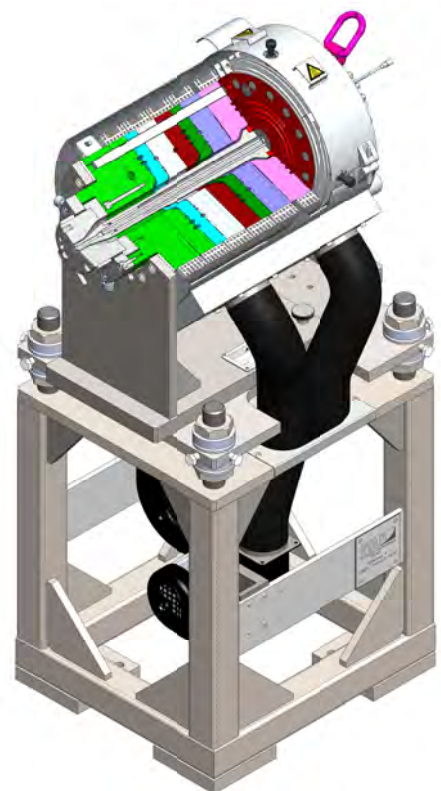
Fünf-Schicht Coextrusionswerkzeug zur Herstellung von Well- und Glatthohren für Automotive Anwendungen
